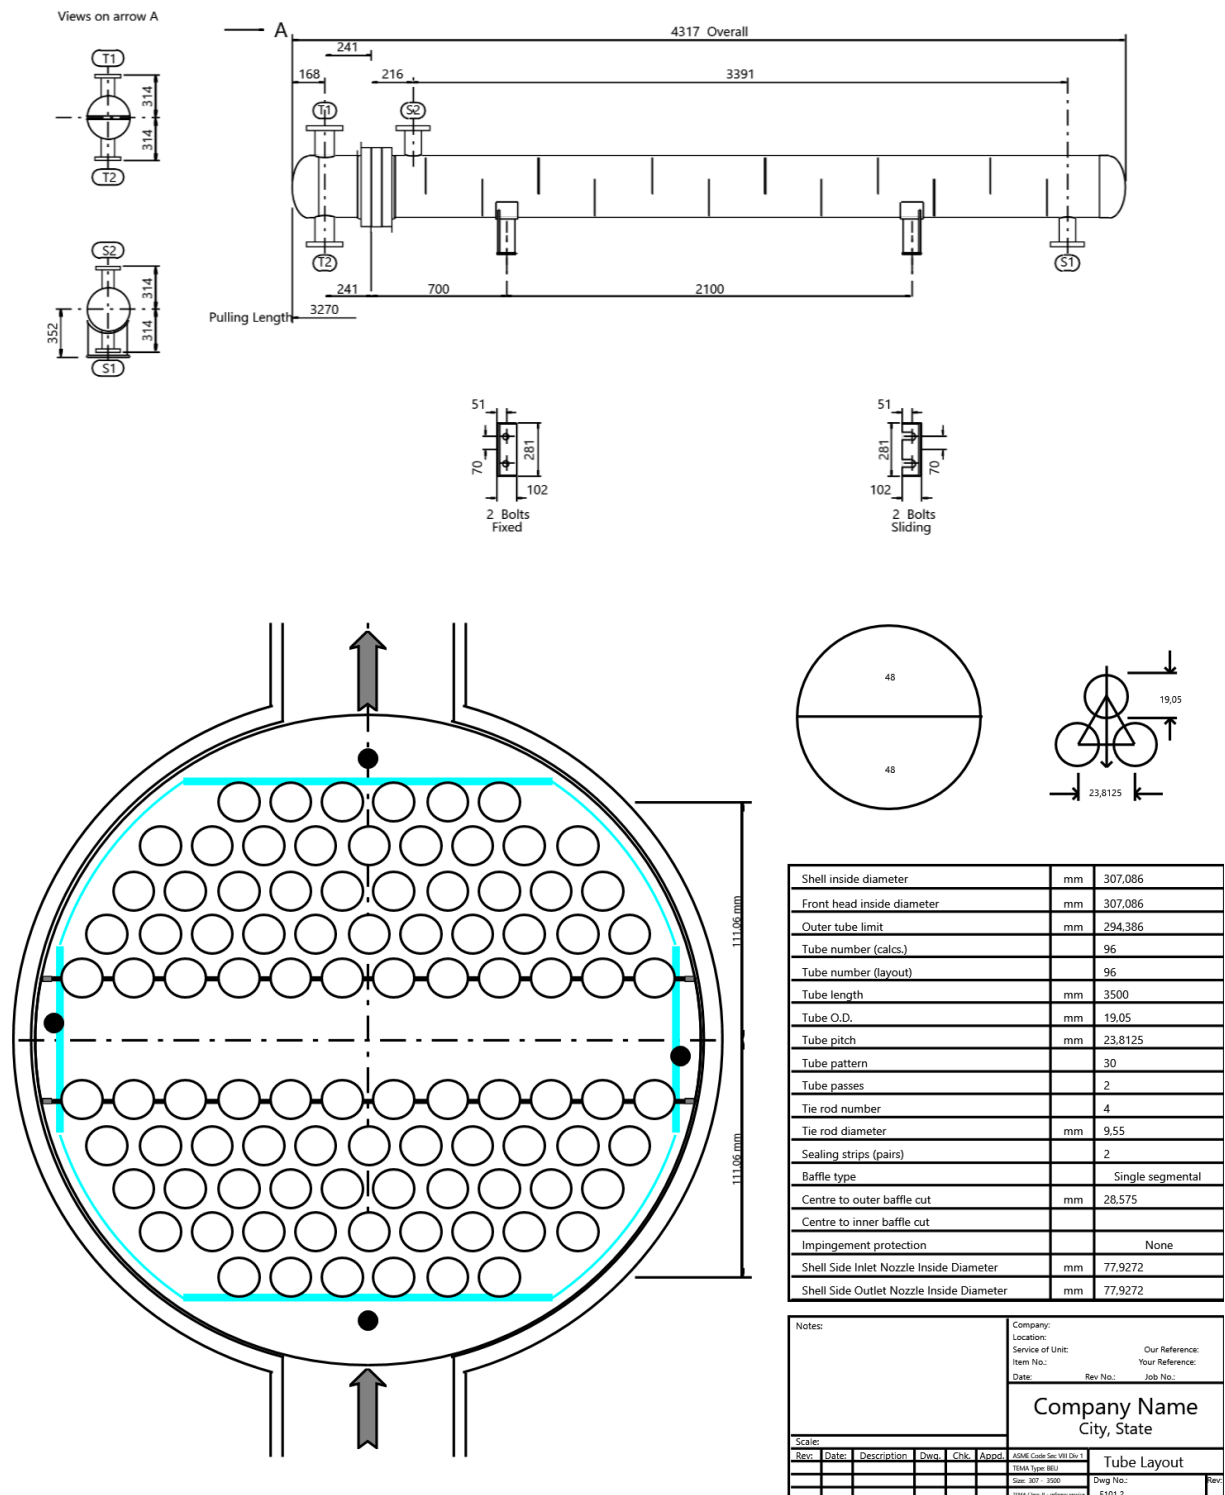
Dimensions i LayOut dels tubs del bescanviador BEU E-101.
